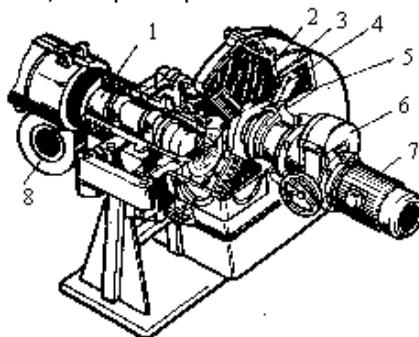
Установка для гранулирования: 1 – подающий шнек, 2 – фильера, 3 – кожух гранулятора, 4 – рубящий нож, 5 – вал, 6 – редуктор, 7 – электродвигатель, 8 - вентилятор
